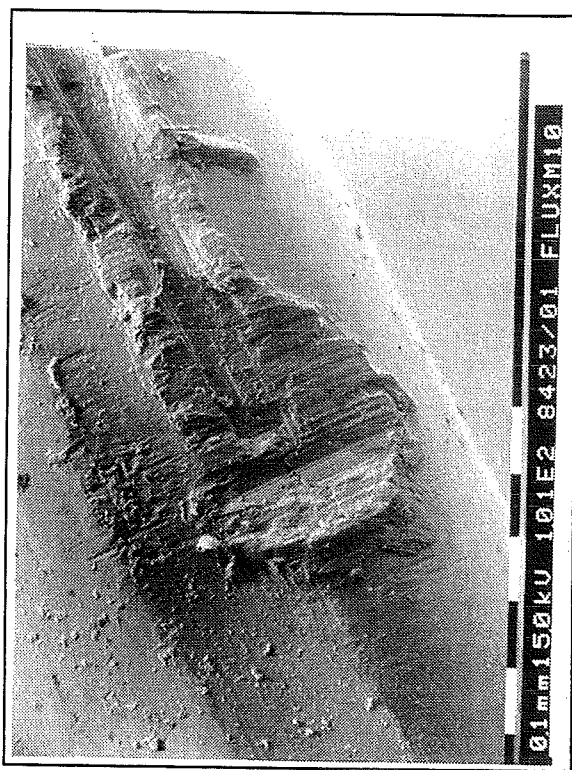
beschadiging op de lasdraad fluxofil, 100 X vergroot.
